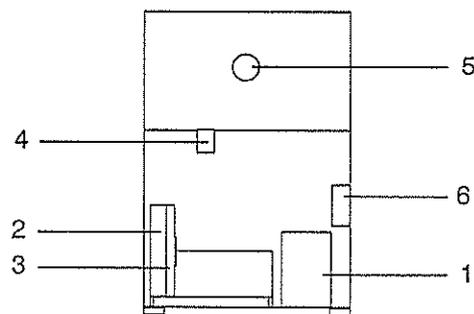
Maschinenteil VMT 04/16 - Rückansicht
